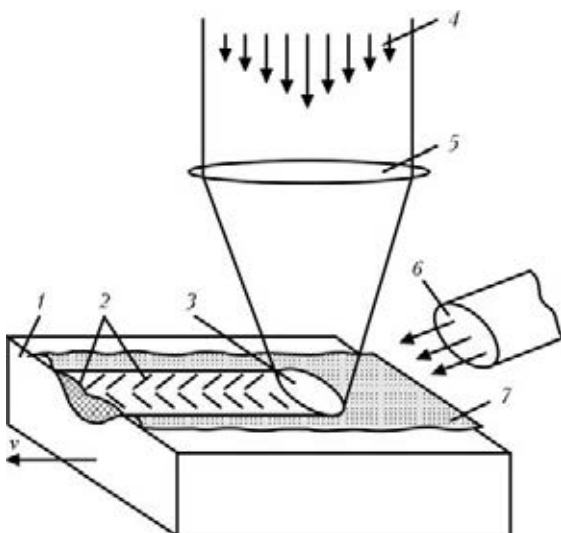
Схема процесса лазерного легирования [12]: 1 — образец, движущийся со скоростью  $v$ ; 2 — легированная дорожка; 3 — ванна расплава; 4 — лазерный пучок; 5 — фокусирующая система; 6 — защитный газ; 7 — легирующая обмазка
